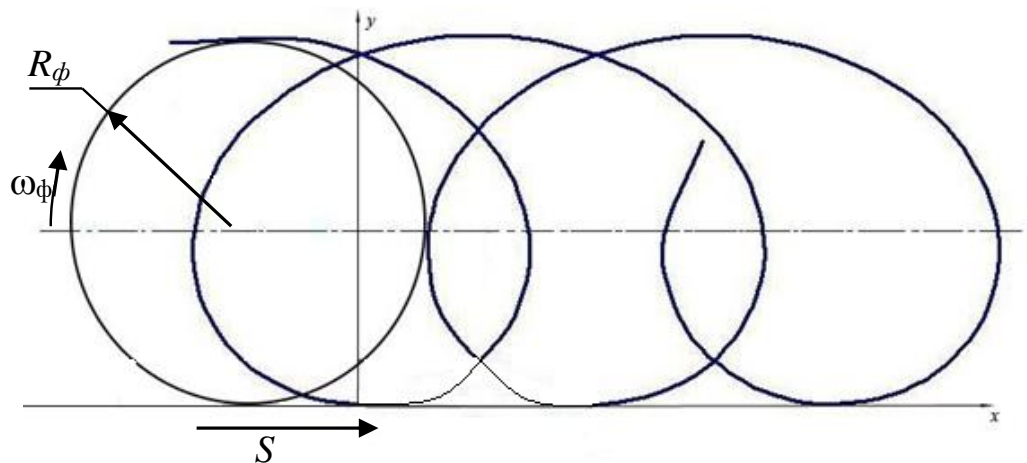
Траєкторія руху фрези при попутному фрезеруванні
